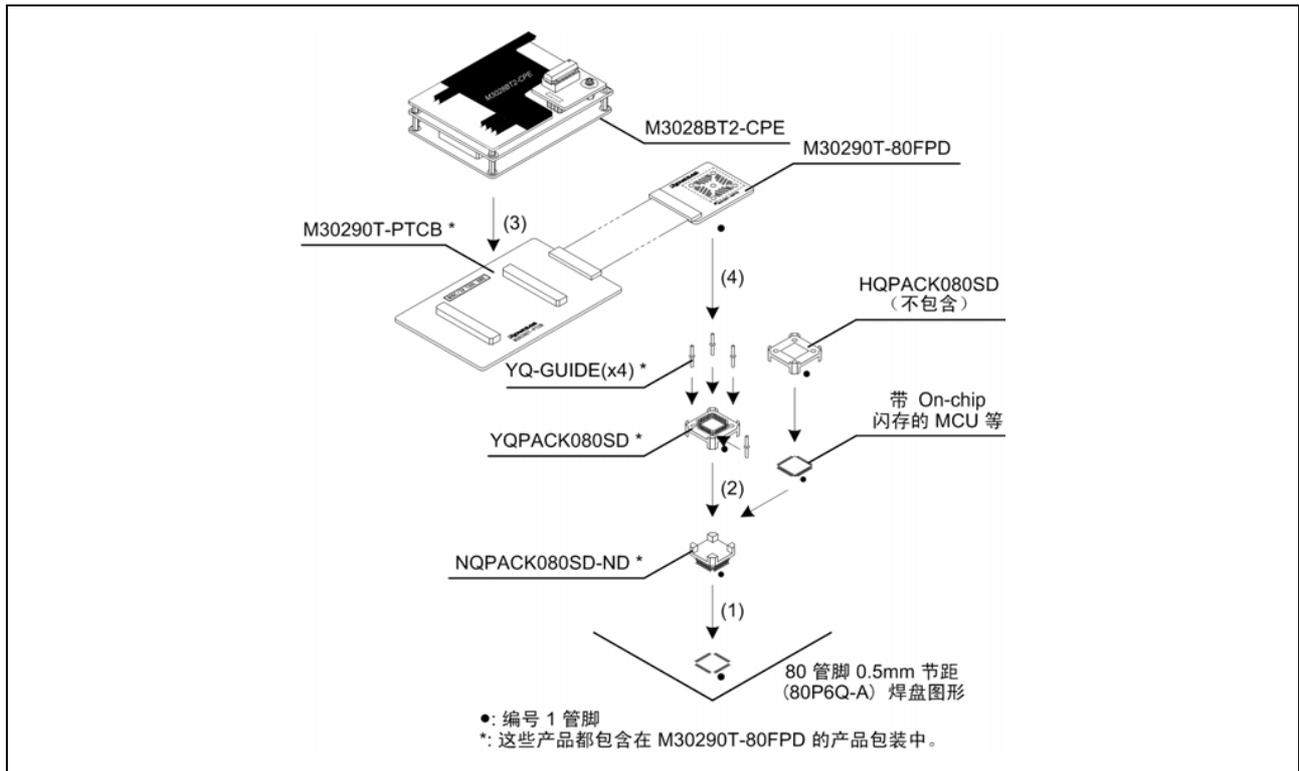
80 管脚 0.5mm 节距焊盘图形的连接
